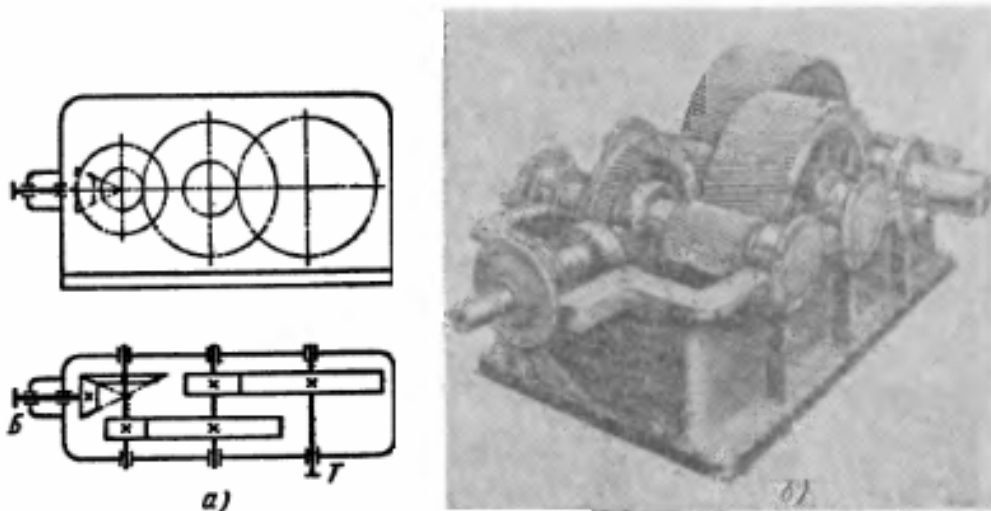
Коническо-цилиндрический трехступенчатый горизонтальный редуктор:
